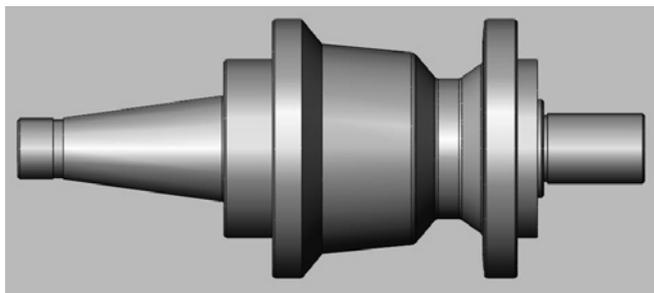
Трехмерная модель заготовки корпуса фасонной фрезы
